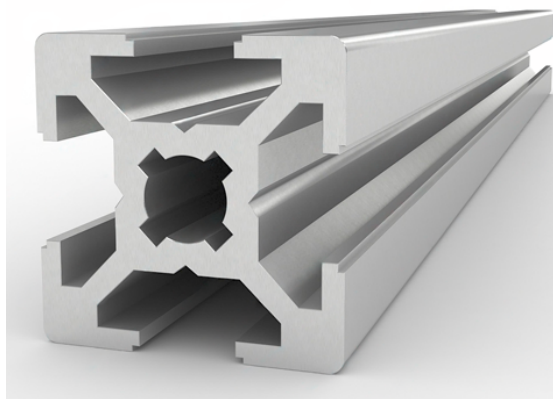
Зовнішній вигляд верстатного алюмінієвого профілю
